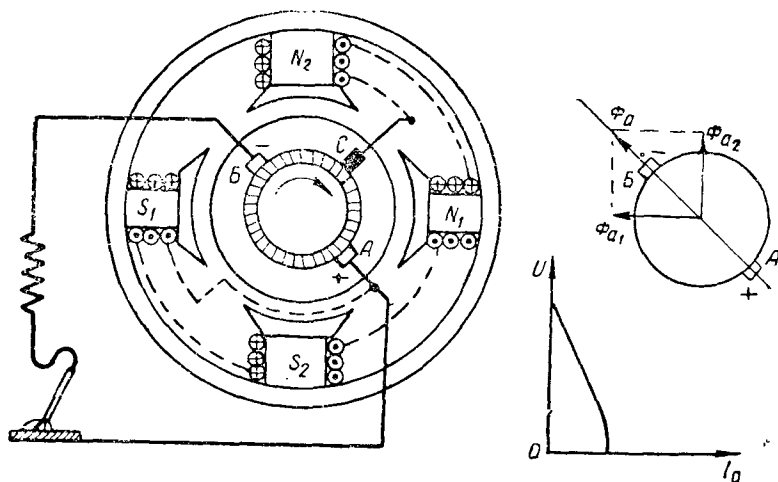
Схема сварочного генератора с поперечным магнитным полем
